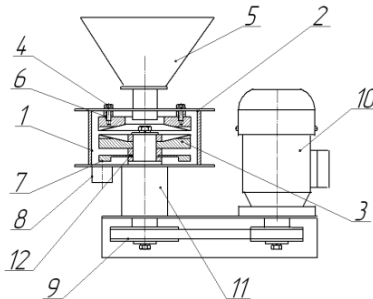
Пристрій дискового подрібнювача: 1 - робоча камера; 2 - верхня кришка; 3 - нижній диск; 4 - болти регулювальні; 5 - завантажувальний бункер; 6 - верхній диск; 7 - активатор; 8 - патрубок; 9 - ремінна передача; 10 - двигун; 11 - корпус підшипників; 12 – втулка
